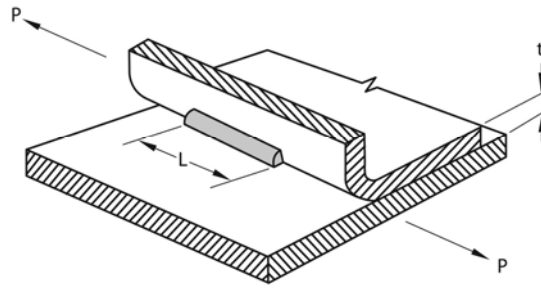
Cortante en soldadura abocinada en media V
